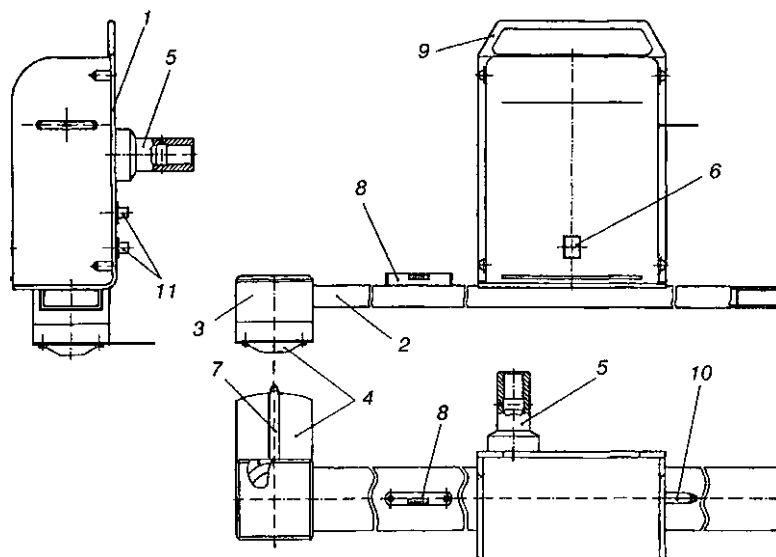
Измерительный блок передний станда КДС 5К фирмы АМД (Россия): 1 — корпус с датчиками развала, наклона и поворота; 2 — штанга; 3 — корпус с датчиками схождения; 4 — крышка датчика схождения; 5 — посадочная втулка; 6 — кнопка; 7 — рычаг ротора датчика схождения; 8 — пузырьковый уровень; 9 — ручка; 10 — рычаг ротора датчика поворота; 11 — разъемы
